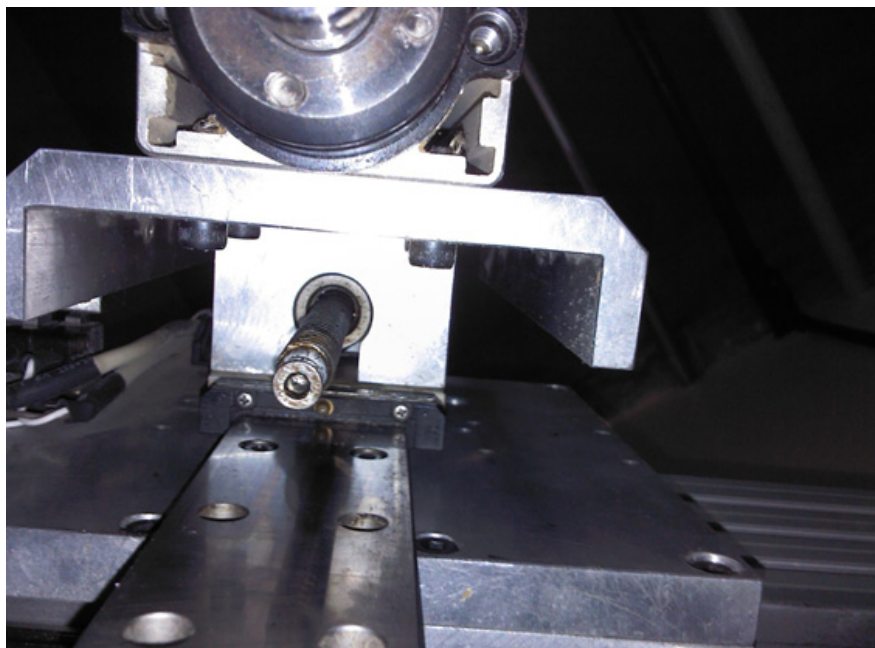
Motor de passo, acoplamento e fuso montados abaixo da mesa.
